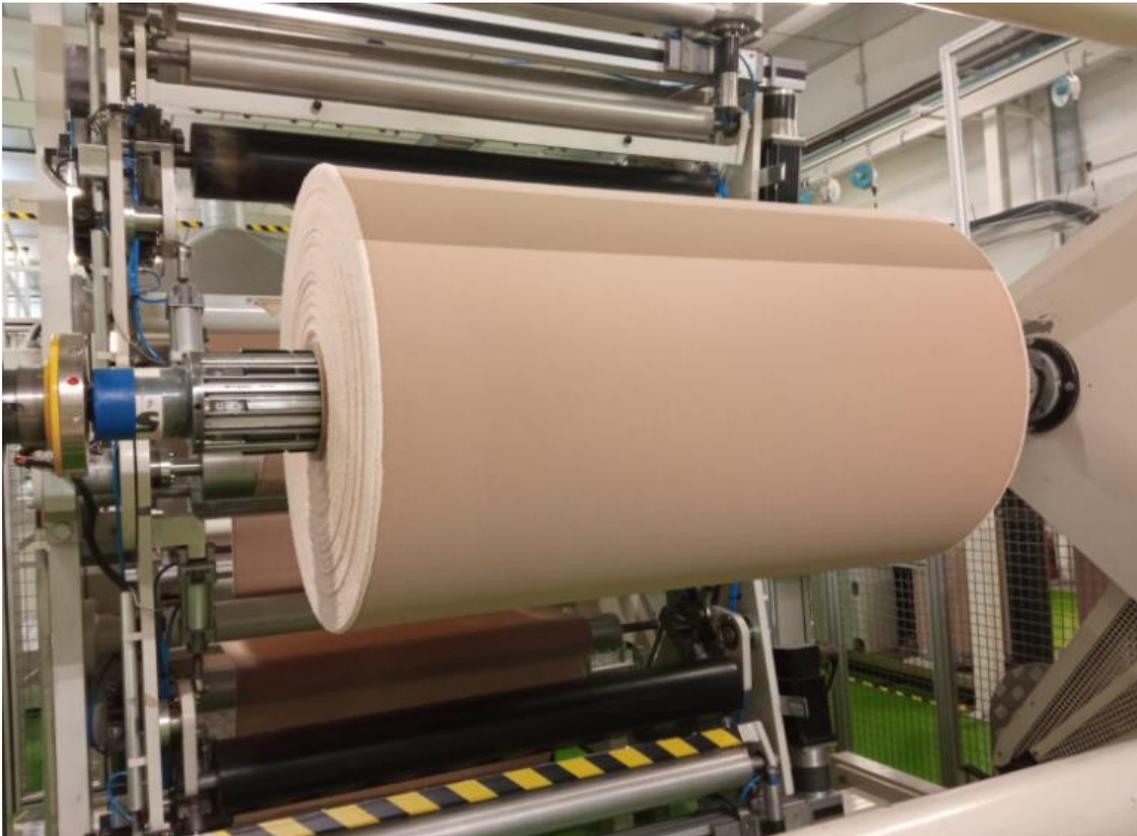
Bobina de Soporte en máquina Hotmelt.
